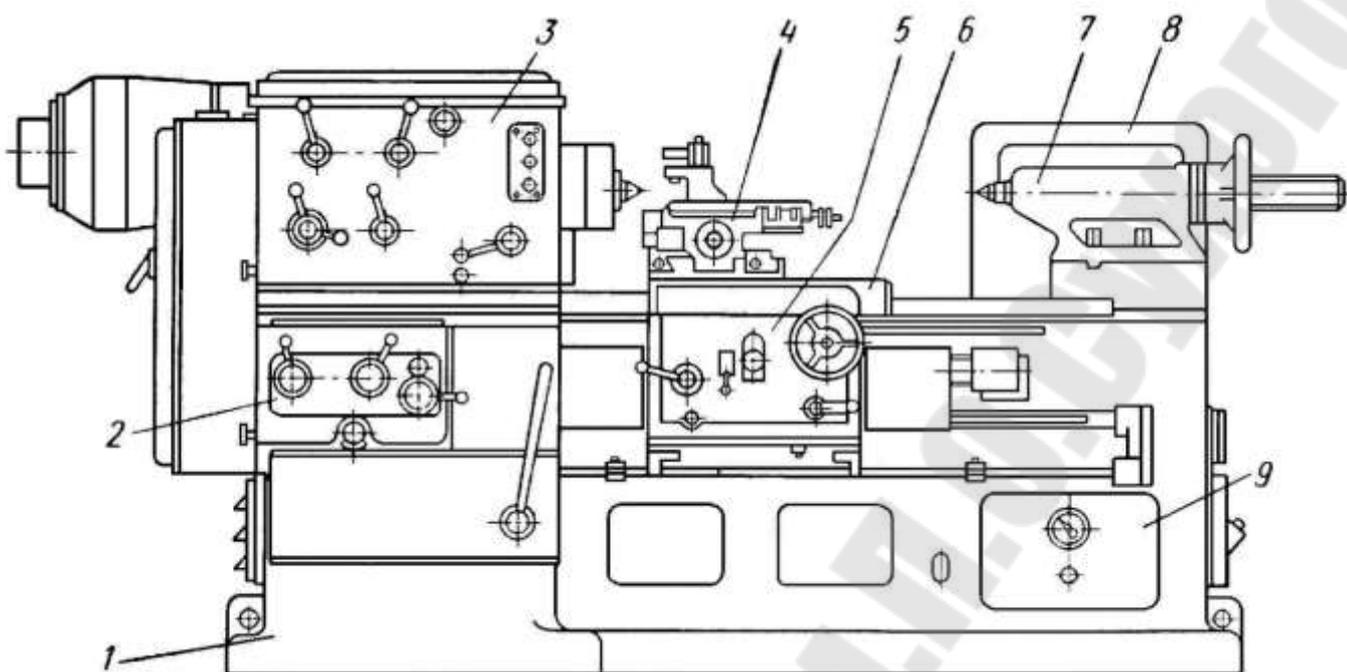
Эскиз общего вида универсального токарно-затыловочного станка модели 1Б811:
